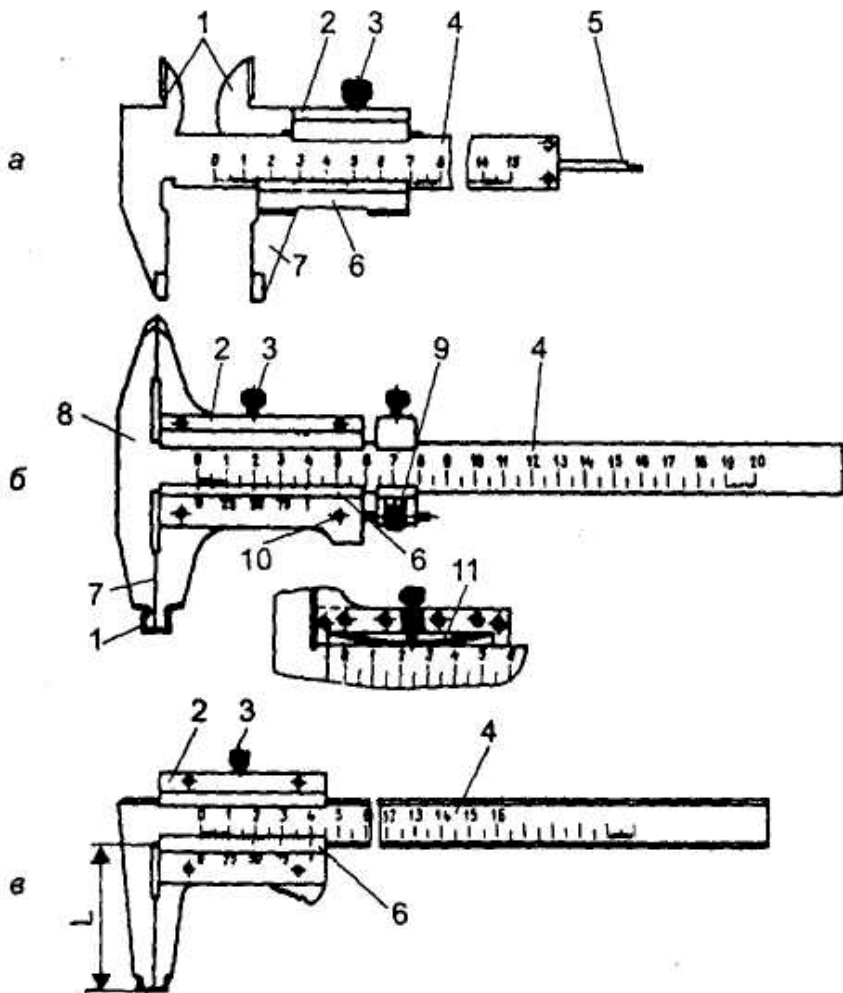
Штангенциркули: а – ШЦ-I; б - ШЦ-II; в - ШЦ-Ш: 1 - губки для внутренних измерений; 2 - рамка; 3 - винт; 4 - штанга; 5 - ножка глубиномера; 6 - нониус; 7 - губки для наружных измерений; 8 - разметочные губки; 9 - микроподача; 10 - винты для крепления нониуса; 11 - пружина
